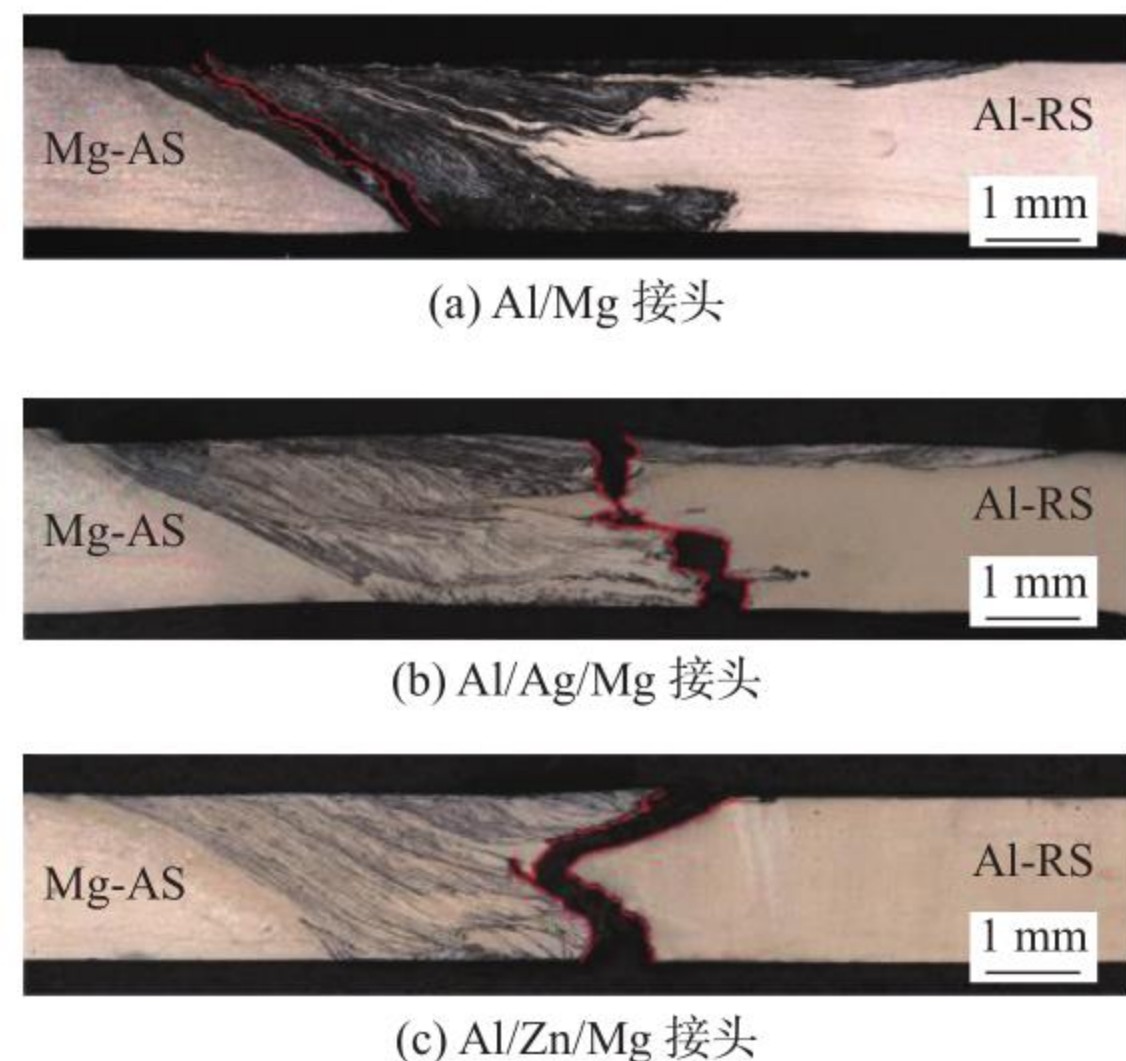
接头断裂截面 Fig. 11 Fracture section of weld joint. (a) Al/Mg joint; (b) Al/Ag/Mg joint; (c) Al/Zn/Mg joint
